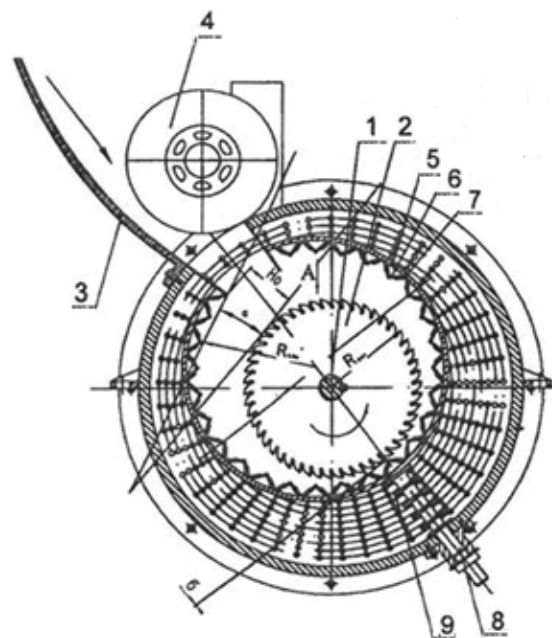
Камера дробления: 1 – ротор; 2 – дисковая фреза; 3 – загрузочный лоток; 4 – подающий валик; 5 – бандаж; 6 – съемный элемент; 7 – неподвижные направляющие; 8 – регулировочное устройство; 9 – пружина
